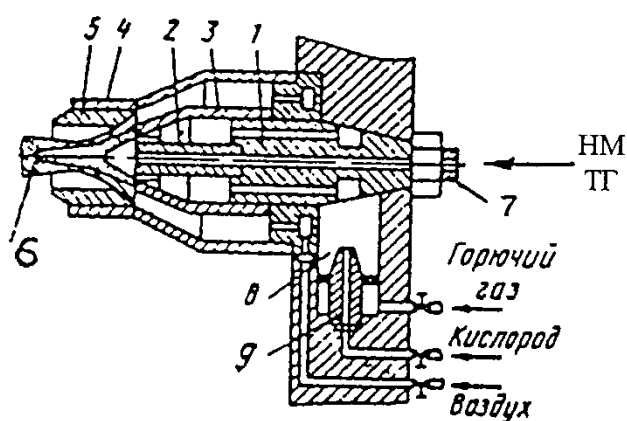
Конструкционная схема газопламенного инжекторного распылителя: 1 – корпус газового сопла; 2 – наконечник сопла; 3 – газовое сопло; 4 – воздушный колпак; 5 – воздушное обжимное сопло; 6 – газовое пламя; 7 – канал для подачи напыляемого материала (НМ) и транспортирующего газа (ТГ); 8 – смесительная камера; 9 – инжектор
